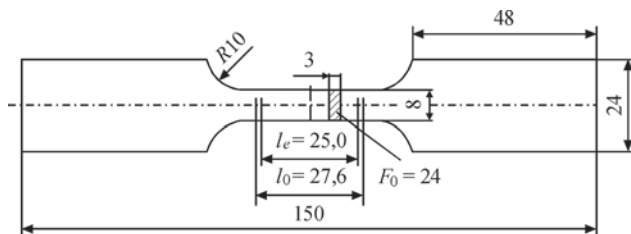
Зразок для випробувань на розтяг: l_e – початкова база тензометра; l_0 – початкова розрахункова довжина; F_0 – початкова площа поперечного перерізу
